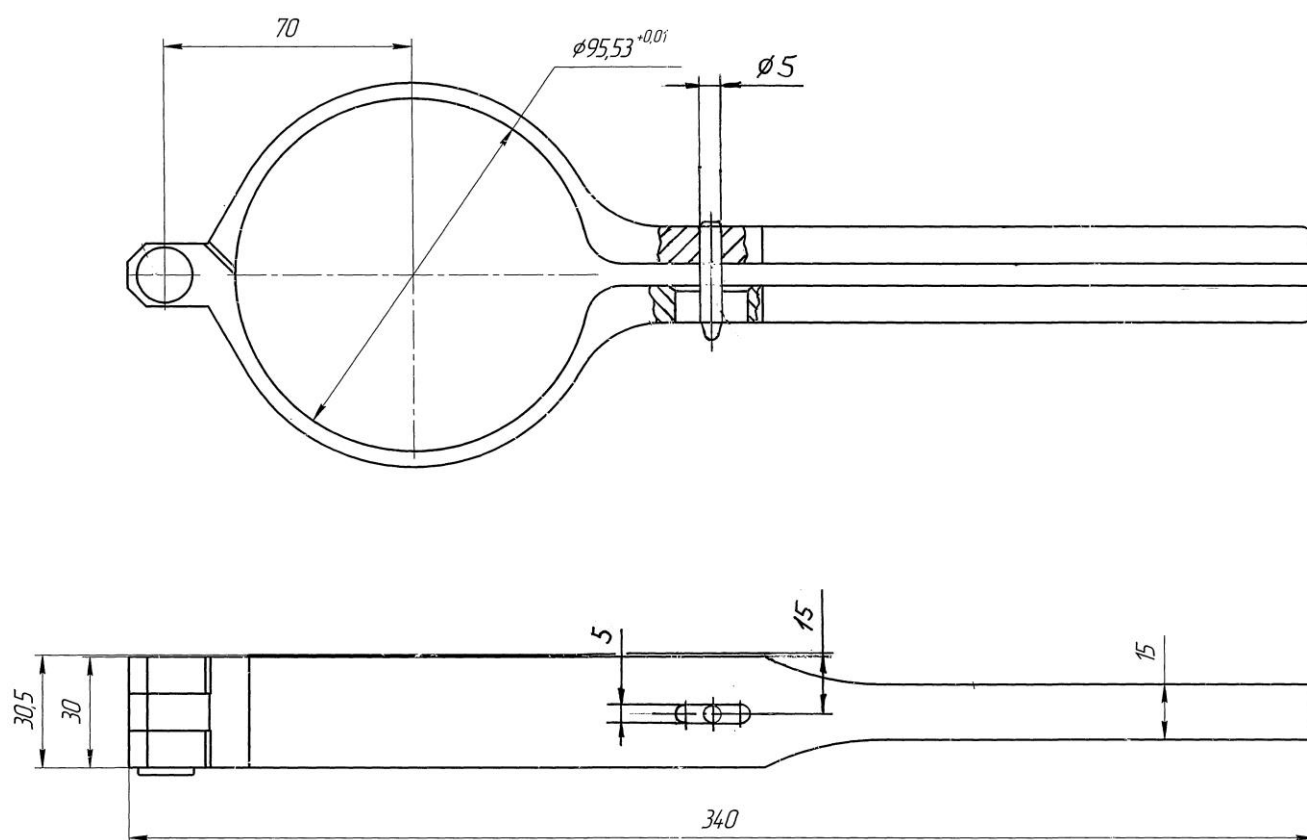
ЗМ 7820-4517, Оправка для сжатия поршневых колец $\varnothing 95,5$ мм
